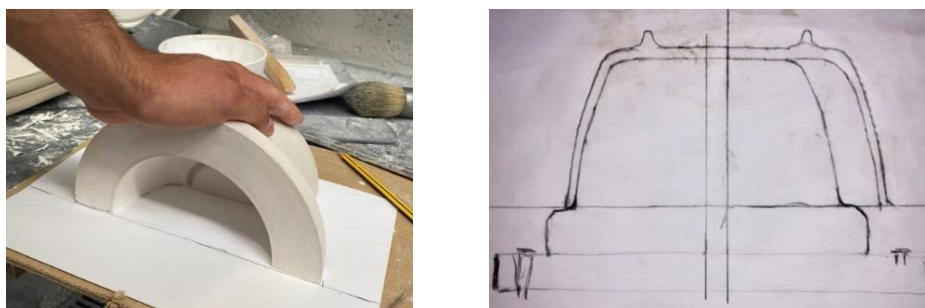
Desenho do calibrador pelo método de fabrico tradicional a partir do primeiro molde de gesso.
